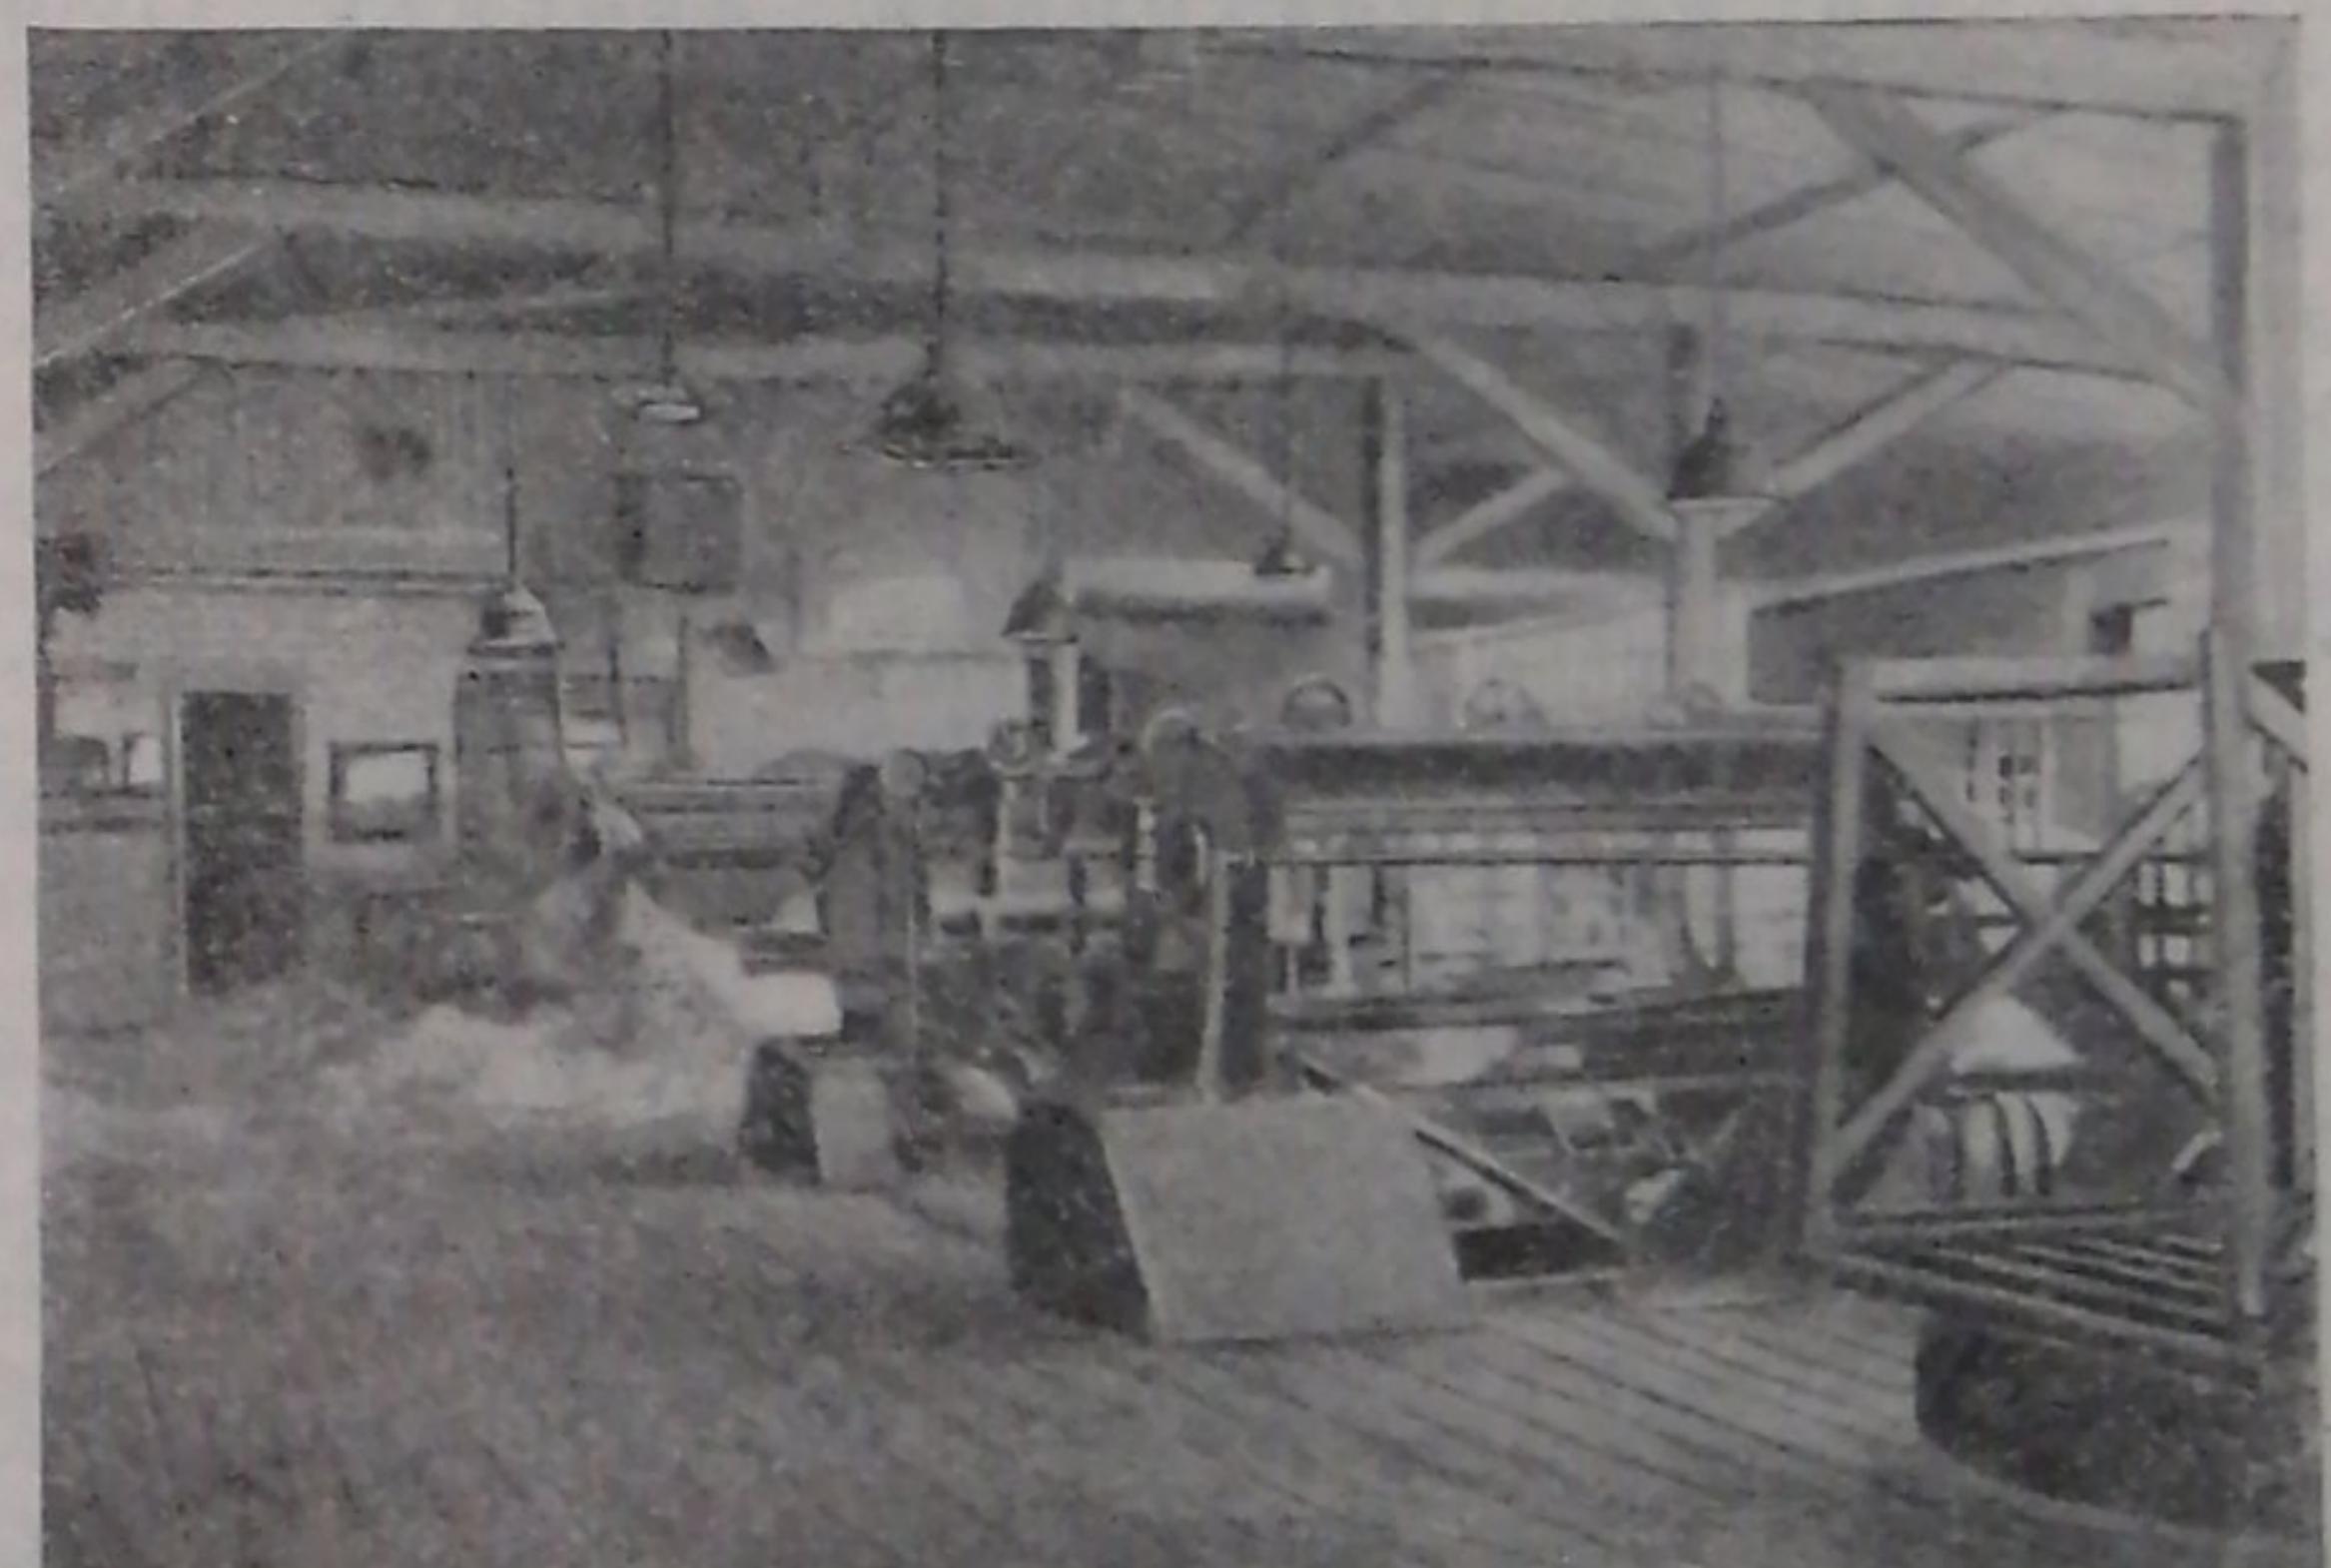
Пролетарский комбинат — одно из передовых деревообрабатывающих предприятий СССР. На рисунке — стружечный цех комбината, оборудованный наиболее современными станками
